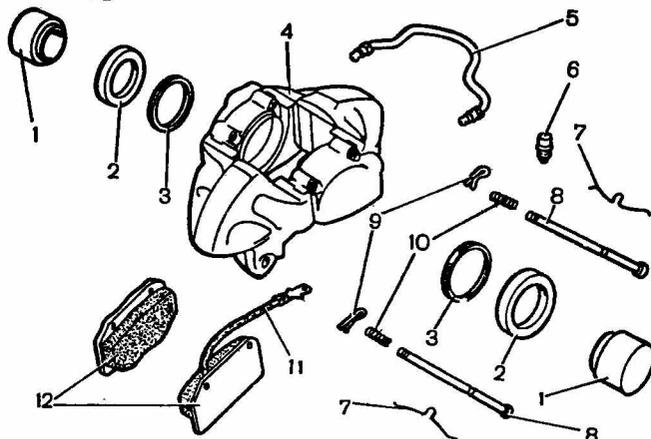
Детали суппорта переднего тормоза: 1 - поршень; 2 - пылезащитный колпачок; 3 - уплотнительное кольцо; 4 - суппорт с цилиндрами; 5 - соединительная трубка тормозных цилиндров; 6 - штуцер выпуска воздуха; 7 - прижимные пружины колодок; 8 - пальцы крепления тормозных колодок; 9 - шплинты; 10 - пружины; 11 - провод сигнализатора износа накладок; 12 - тормозные колодки
